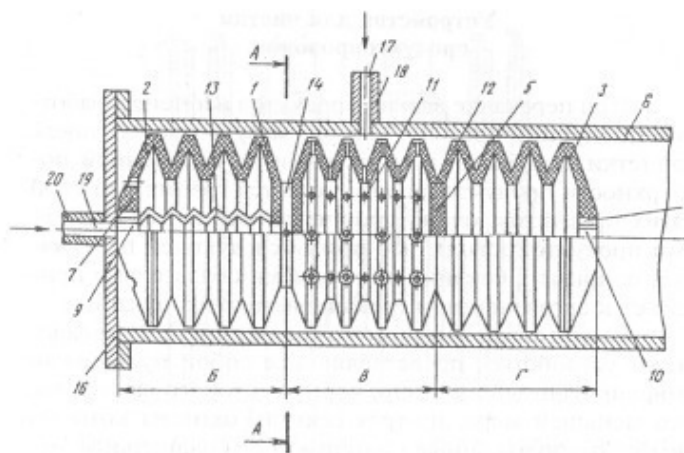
Общий вид устройства для чистки продуктопроводов, где 1 – гофрированный цилиндр; 2, 3 – торцевые крышки; 4, 5 – перегородки; 6 – камера запуска; 7, 8 – штуцера; 9, 10 – резьбовые отверстия; 11, 12, 14 – сквозные отверстия; эластичная трубка; 15 – пазы; 16 – крышка; 17, 19 – отверстия; 18, 20 – штуцера.
